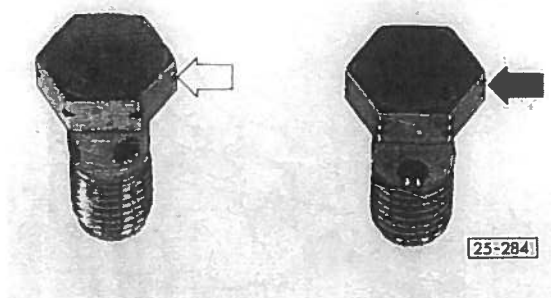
Remplacement de la soupape antiretour du filtre à carburant
